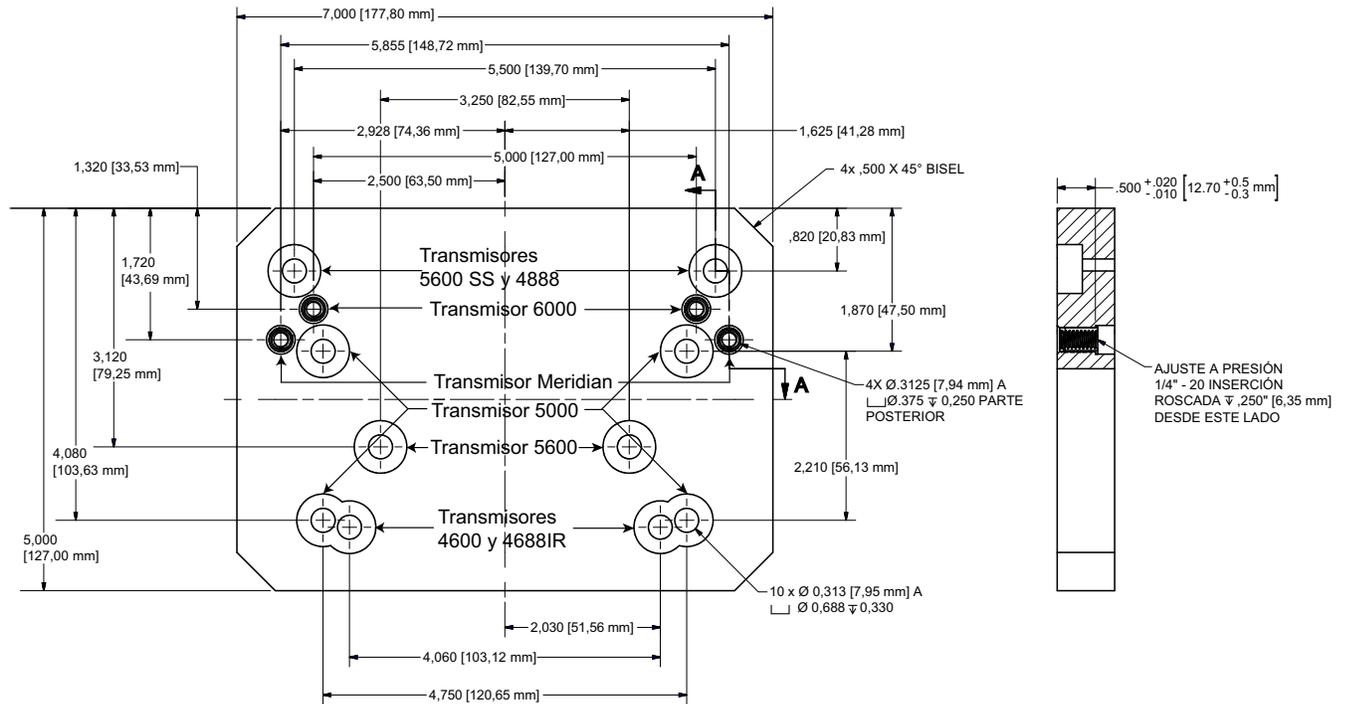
Dimensiones de la placa de montaje de adaptación - HDPE
